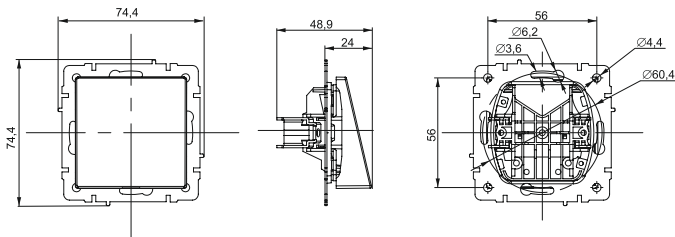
Габаритные и установочные размеры вывода кабеля / Figure 1 – Overall and installation dimensions of the cable outlet / 1-сурет – Кабелді шығарудың габаритті және орнату өлшемдері /
